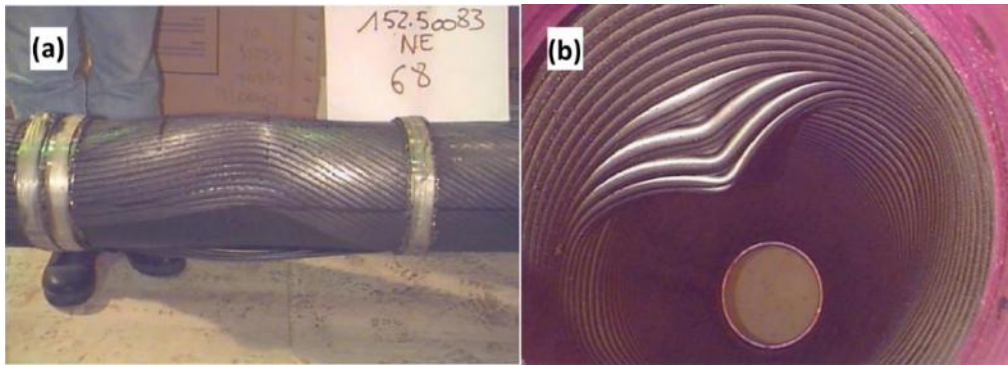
(a) Vista externa e (b) interna de outro colapso hidrostático [49]
